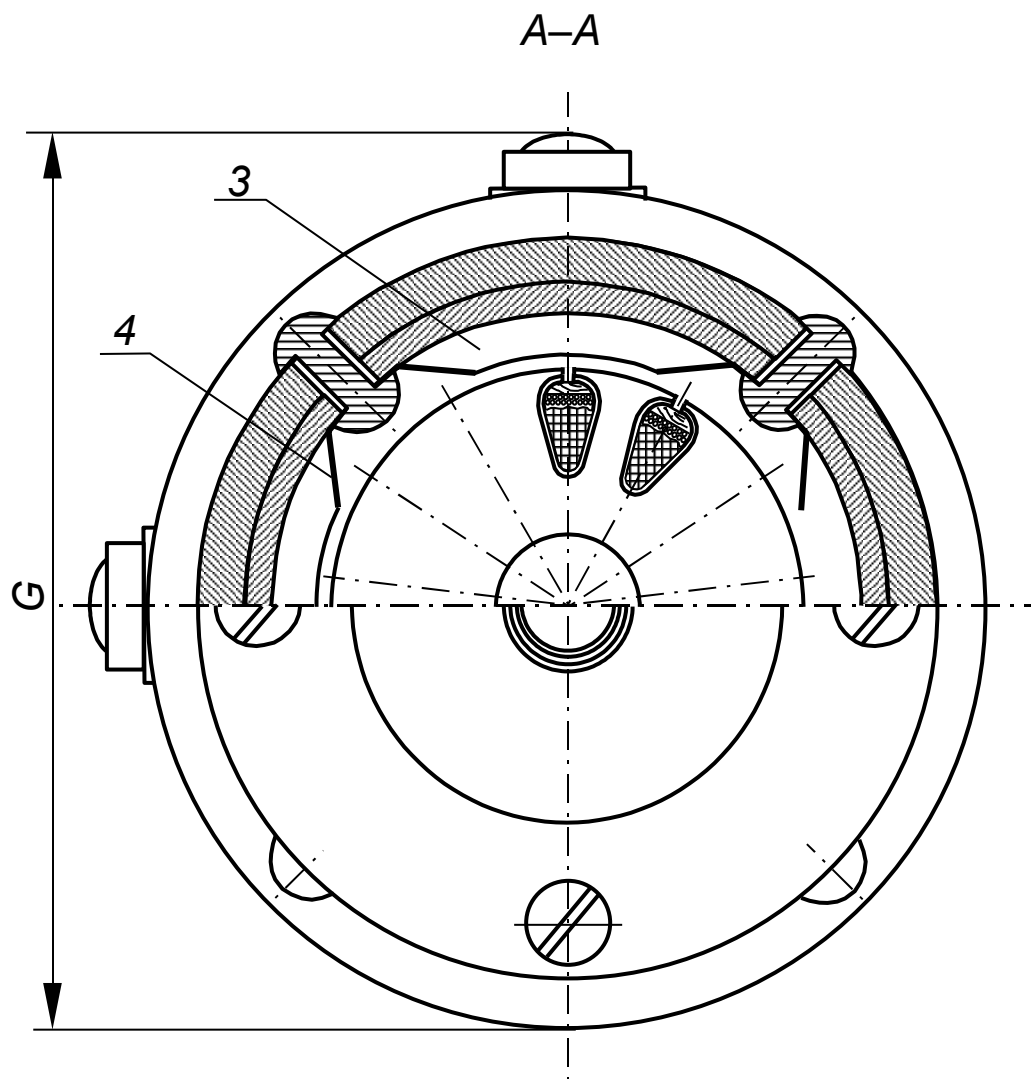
Общий вид двигателя постоянного тока (поперечный разрез)
